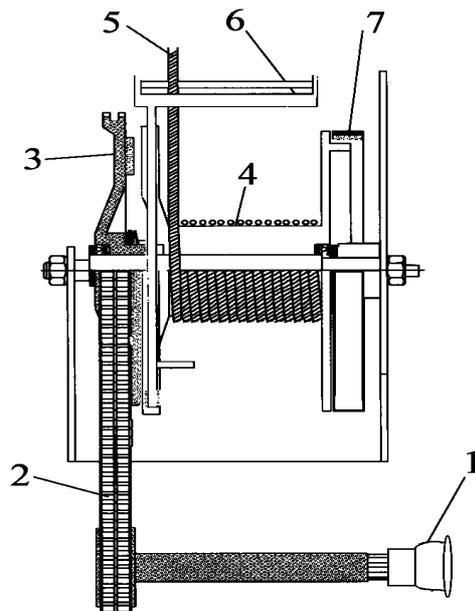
Схема привода лебедки: 1 - вал отбора мощности; 2 - цепной привод; 3 - фрикционный диск; 4 - барабан; 5 - канат; 6 - тормоз барабана; 7 - ленточный тормоз
